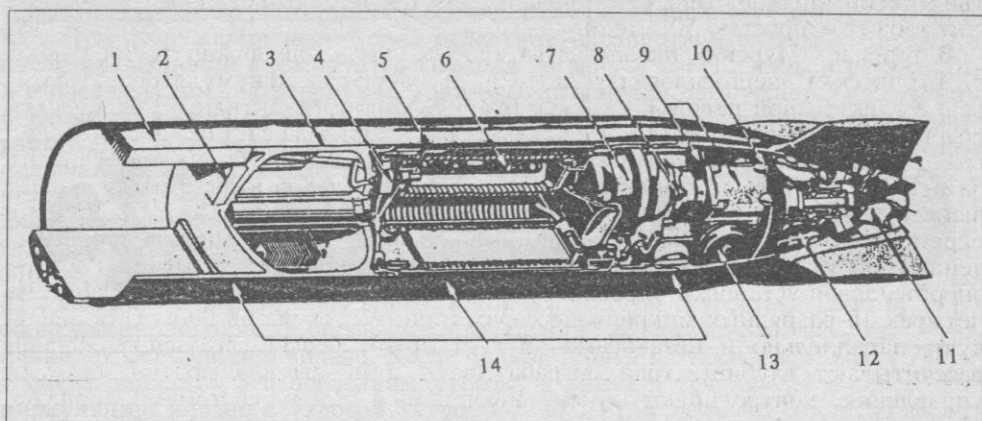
Схема двигательной установки торпеды Mk50: 1 – корпус торпеды; 2 – электронный блок проверки двигателя; 3 – бак окислителя; 4 – система подачи окислителя; 5 – теплообменник; 6 – реактор; 7 – турбина; 8 – редуктор; 9 – генераторы переменного тока; 10 – форсунка быстрого старта; 11 – сопло; 12 – рулевые приводы; 13 – водометный двигатель; 14 – звукоизоляторы
